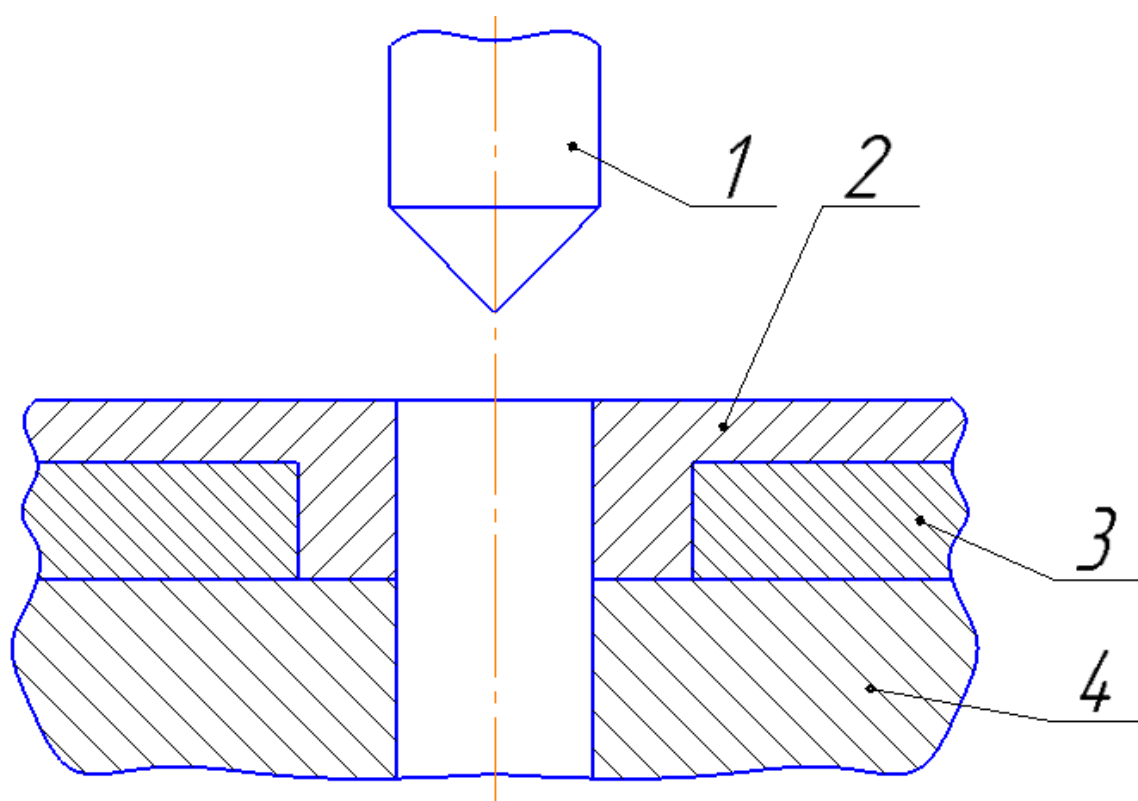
Получение отверстия с отбортовкой[10]: 1 – пуансон; 2 – тонколистовая заготовка; 3 – формообразующая матрица; 4 – обрезающая матрица
